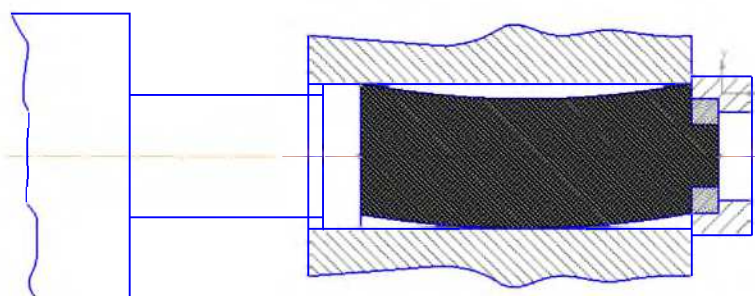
Продольный изгиб во время распрессовки заготовки в контейнере.
